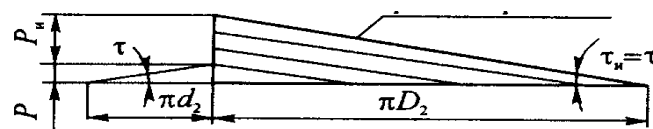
Развертка витка резьбы резьбонакатного ролика и детали
